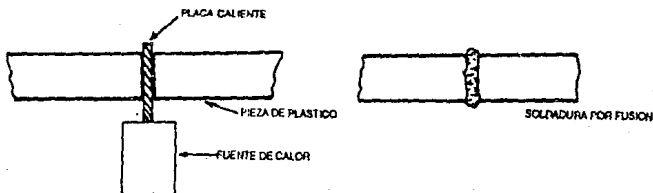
Soldadura por fusión. (Ref. 2).
